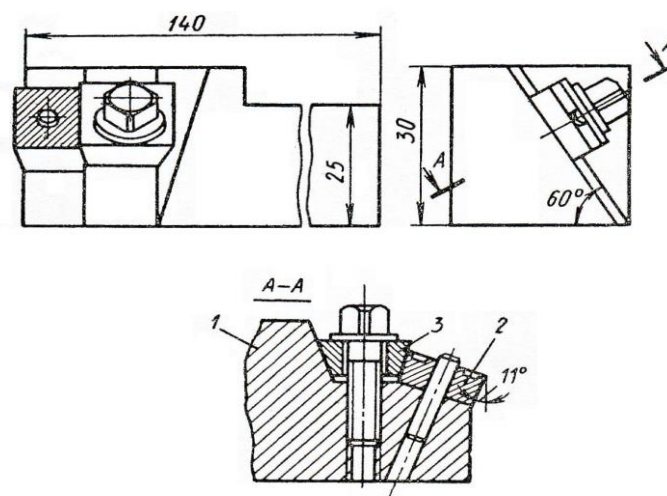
Чистовий різець для гостріння заготовок із нержавіючих сталей
